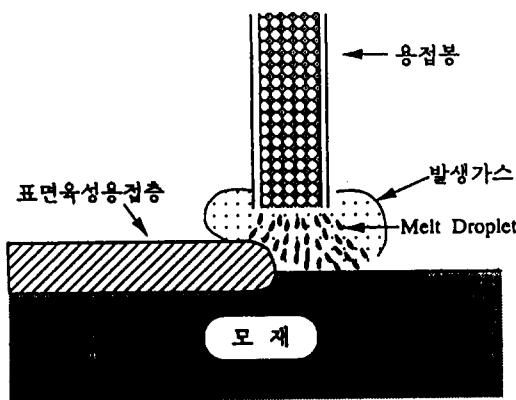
오버레이 용접(Overlay Welding, 일명 Weld Surfacing, Hardfacing, 육성용접) 장면의 도식도.
